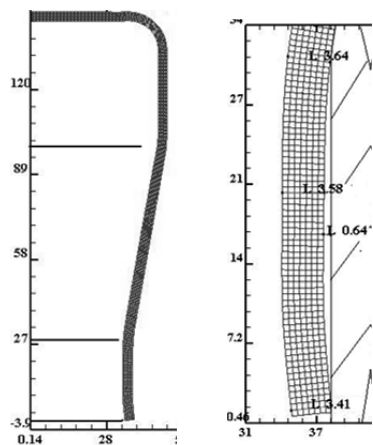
Розміри половини виробу з горловиною і горловини (мм) та загальний вигляд виробу в розрізі при обтиску заготовок з  $S_0/D = 0,03$
